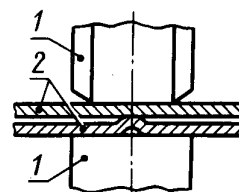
Схема рельефной шовной сварки: 1-ролики; 2-свариваемые детали
